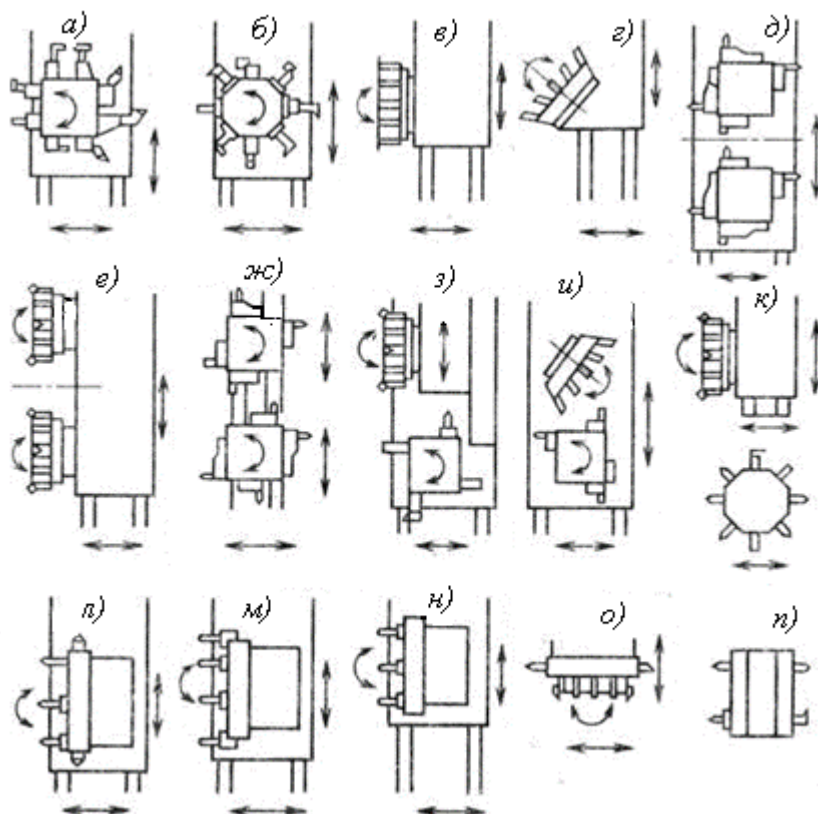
Схемы конструктивного исполнения револьверных головок токарных станков
